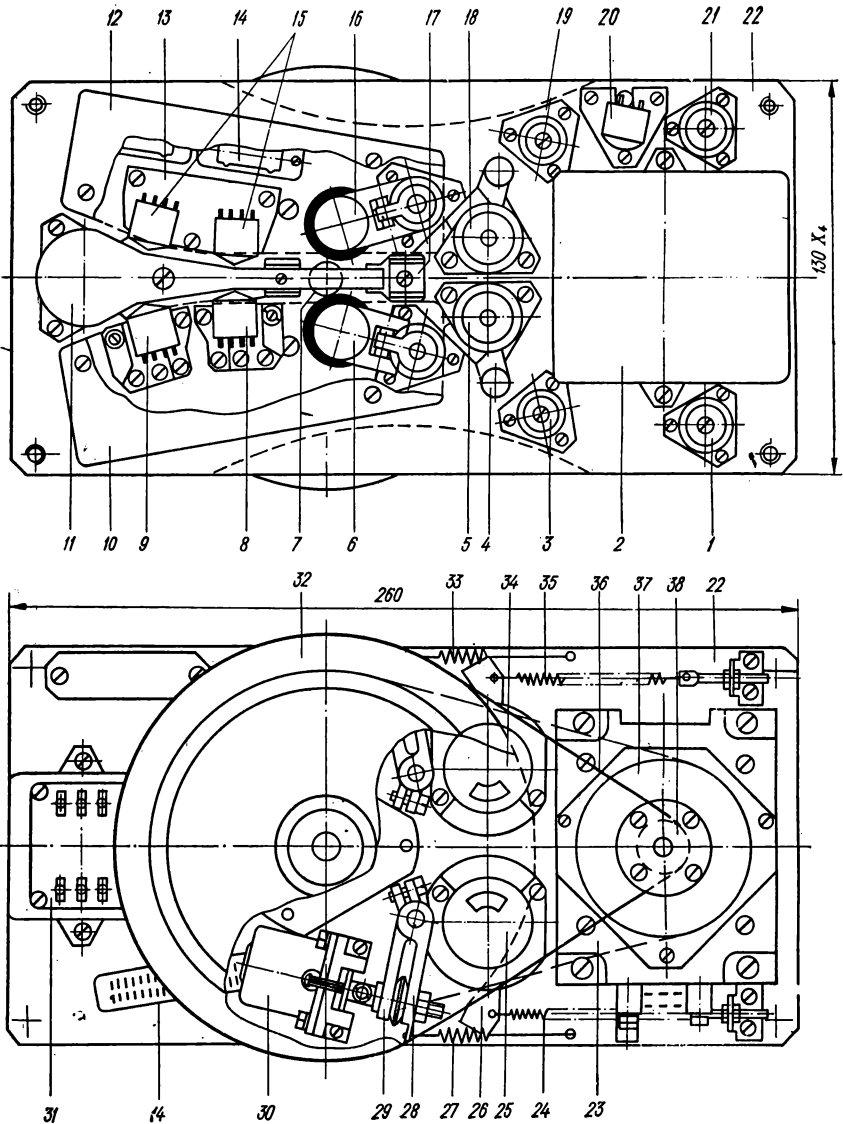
Конструкция блока рабочей зоны с косвенным приводом ведущего вала.
